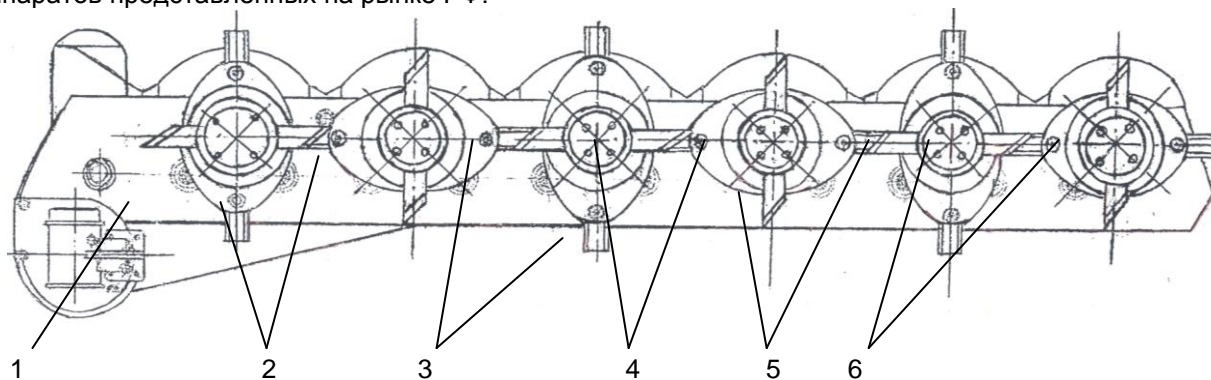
Вид сверху на ротационную косилку КР-2,4М с устройством для деструкции стеблей кормовых трав: 1 – шестеренчатый брус; 2 - диски; 3 - шарнирные ножи; 4 – барабаны; 5 – била-ножи; 6 – крышки барабанов
